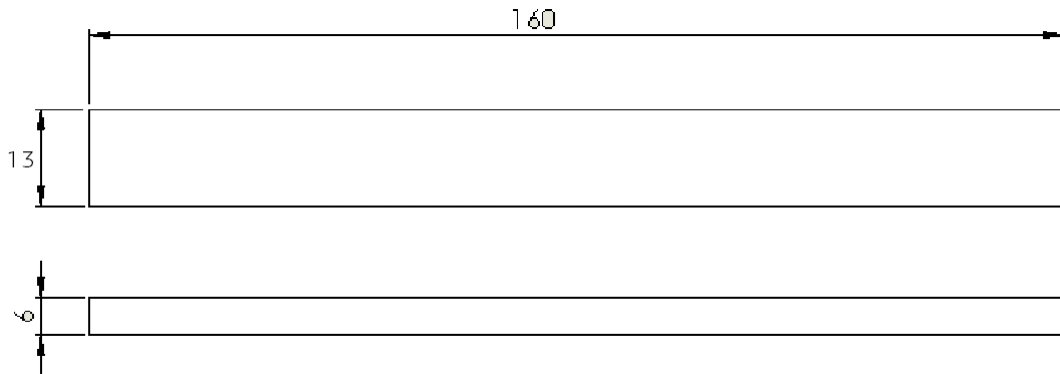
Dimensiones de la Probeta para el ensayo a Flexión [5].
